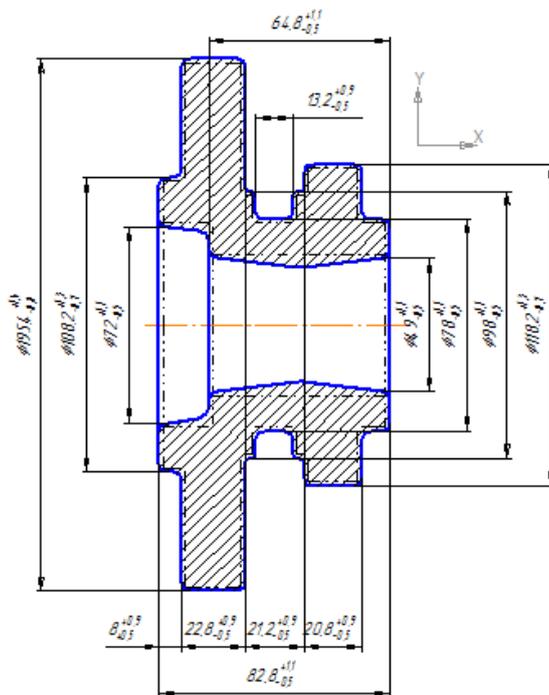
Эскиз заготовки полученной методом закрытой штамповки
